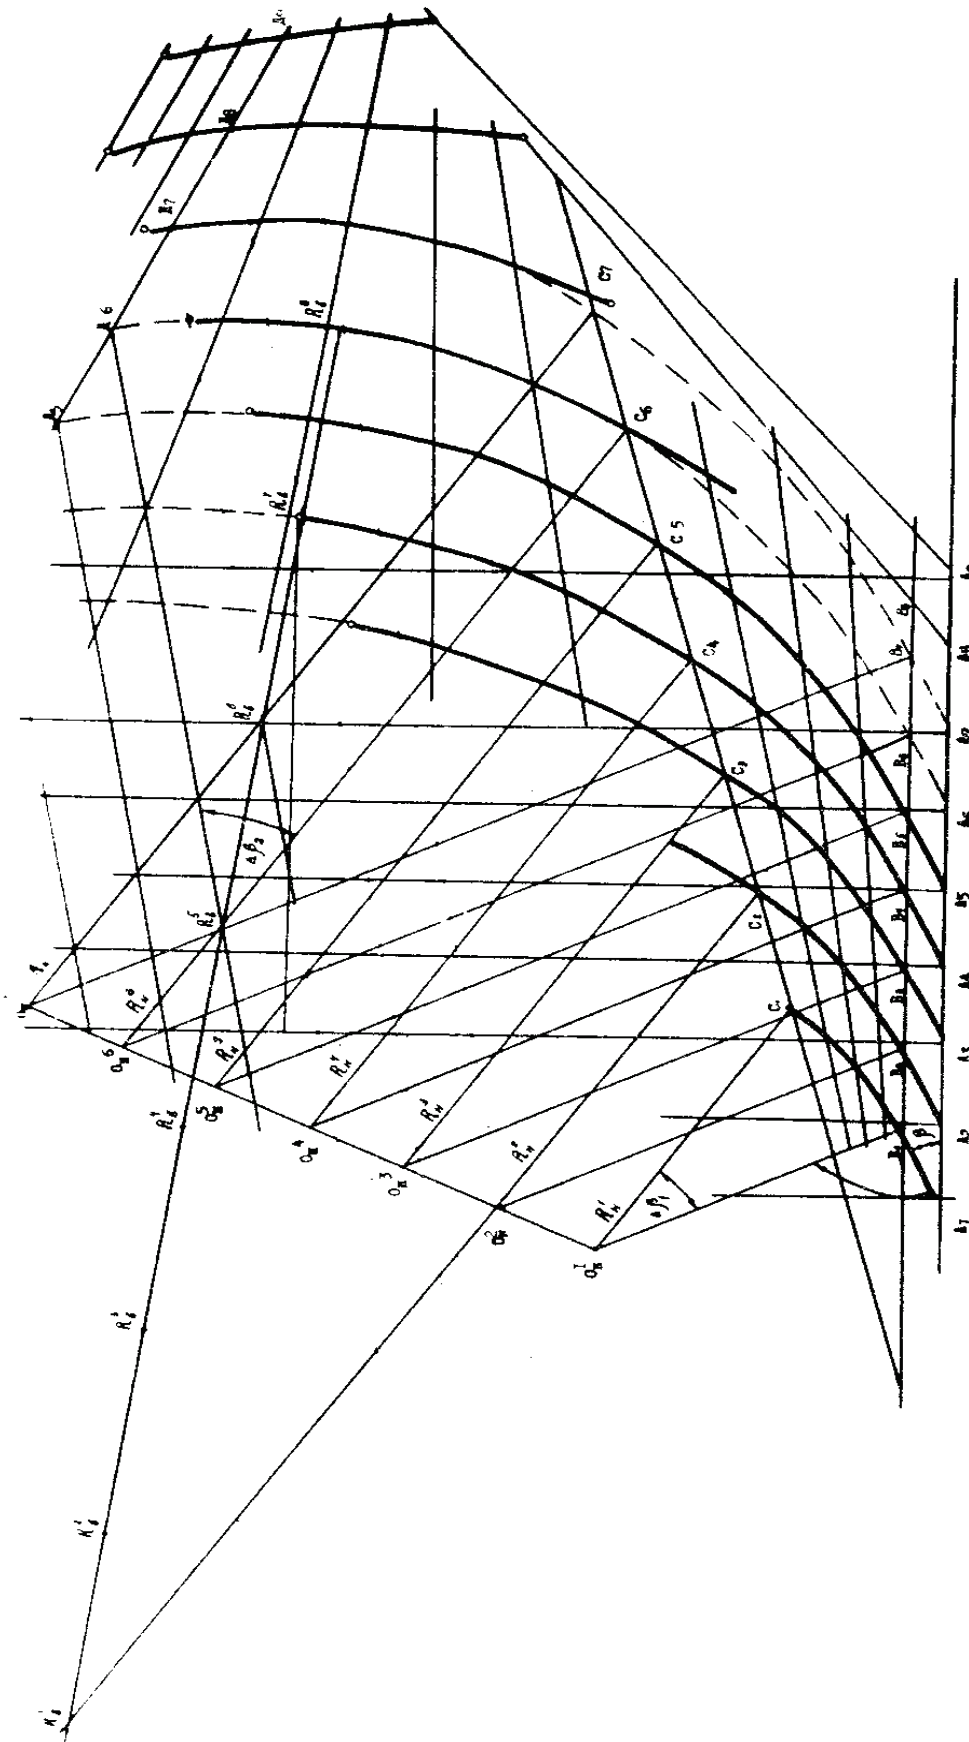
Побудова твірних поверхні поліці швидкісного корпусу
